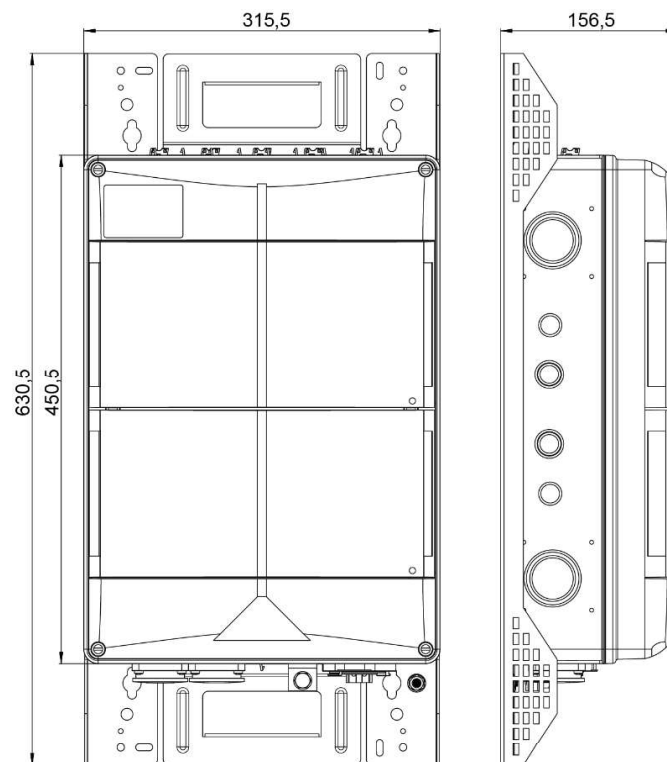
Front- und Seitenansicht gesis® WIV, Höhe 630 mm
